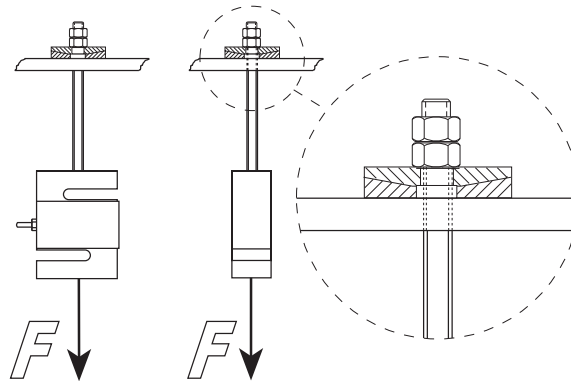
Módulo de Pesaje Tipo S (S-Beam)
